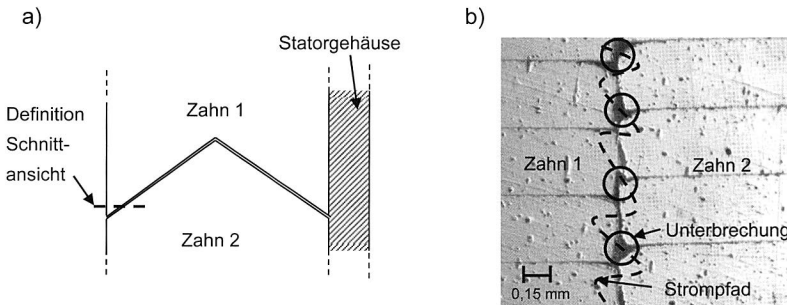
Versatz zwischen zwei Statorzähnen; a) Draufsicht, Definition Schnittansicht, b) Schnittansicht mit Unterbrechungen des Strompfades
